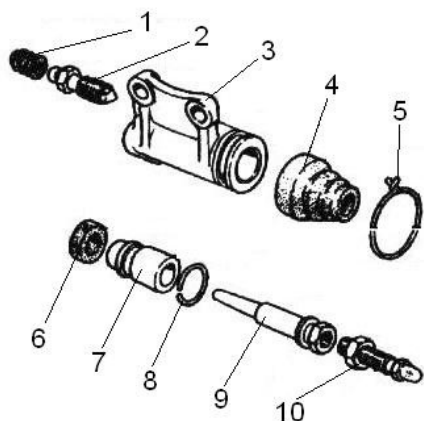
Детали цилиндра привода выключения сцепления (рабочего цилиндра).
